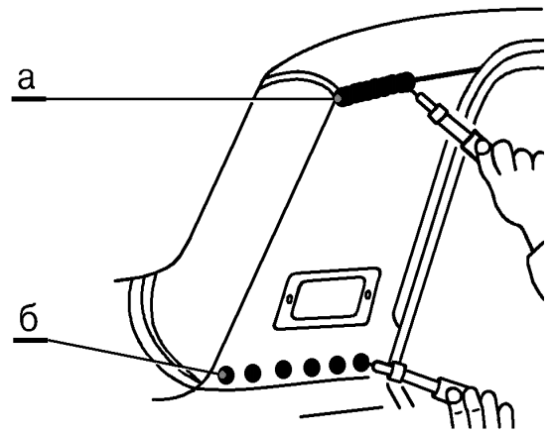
Процес зварювання а – суцільним швом, б – точкове зварювання в напуск по отворах
